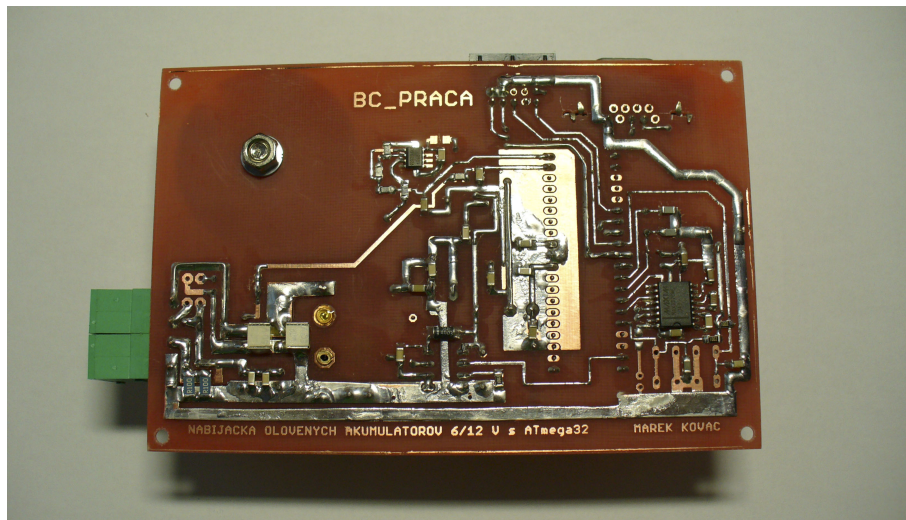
Pohľad zo strany spojov (BOTTOM), skutočný rozmer 136×86 mm
